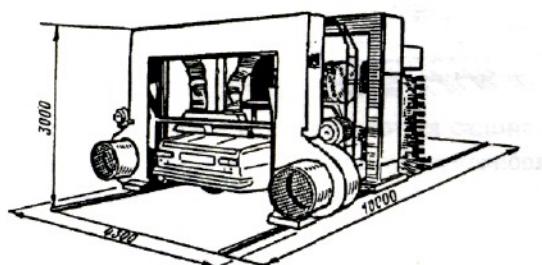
Моечная установка GM-100, сушкой GS-100, с раздвижными воздушными коллекторами
